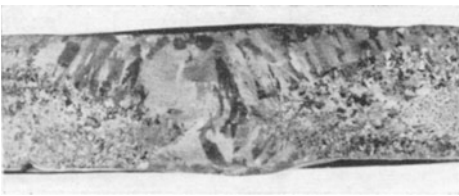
Querschnitt einer Kupferschweißnaht (Schliffbild).
